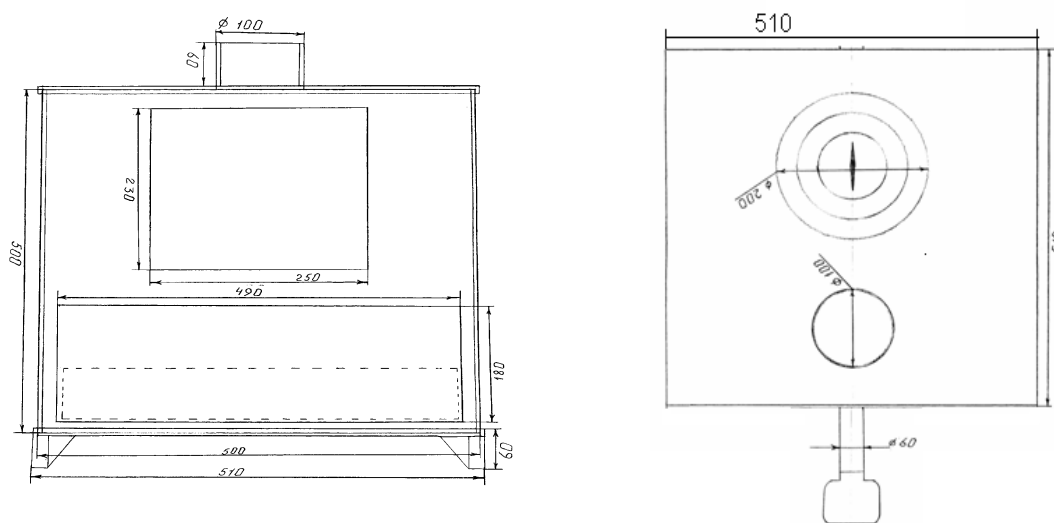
Габаритные размеры печи (вид сбоку и сверху)
